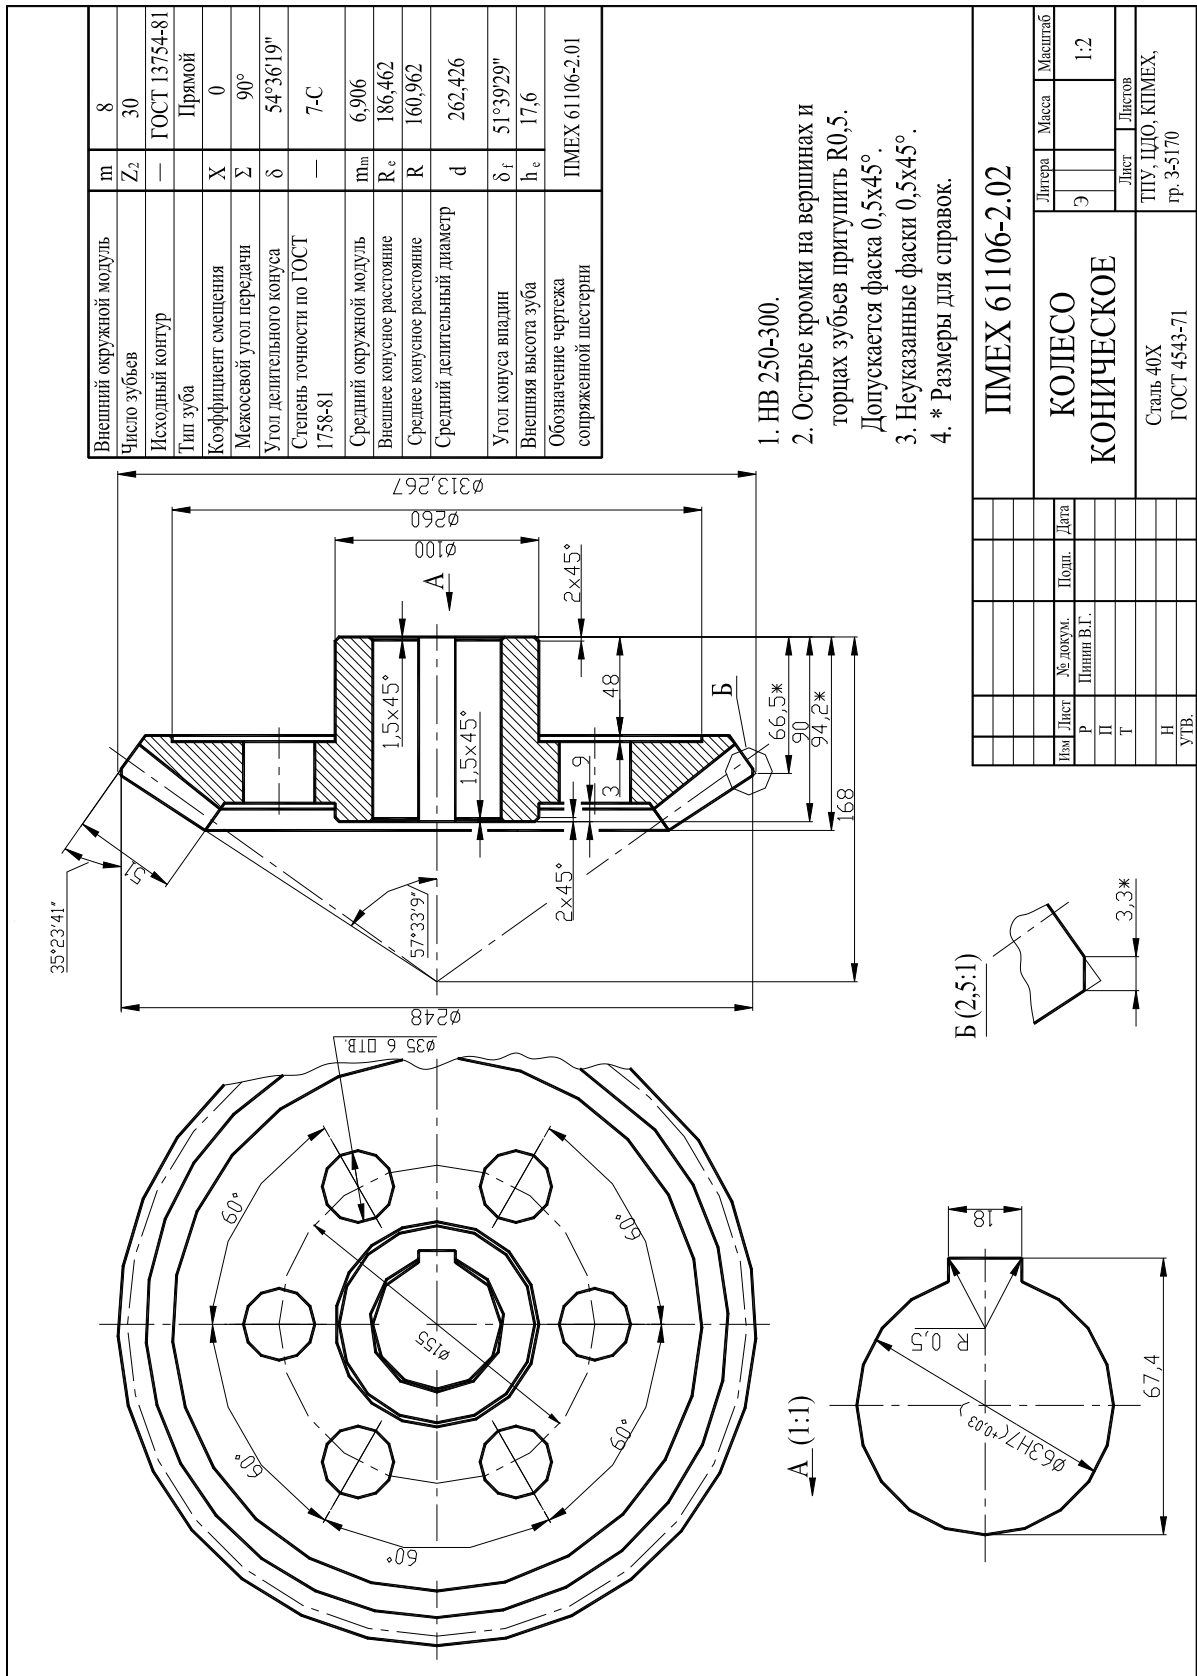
Пример выполнения эскизного чертежа эвольвентного конического зубчатого колеса
